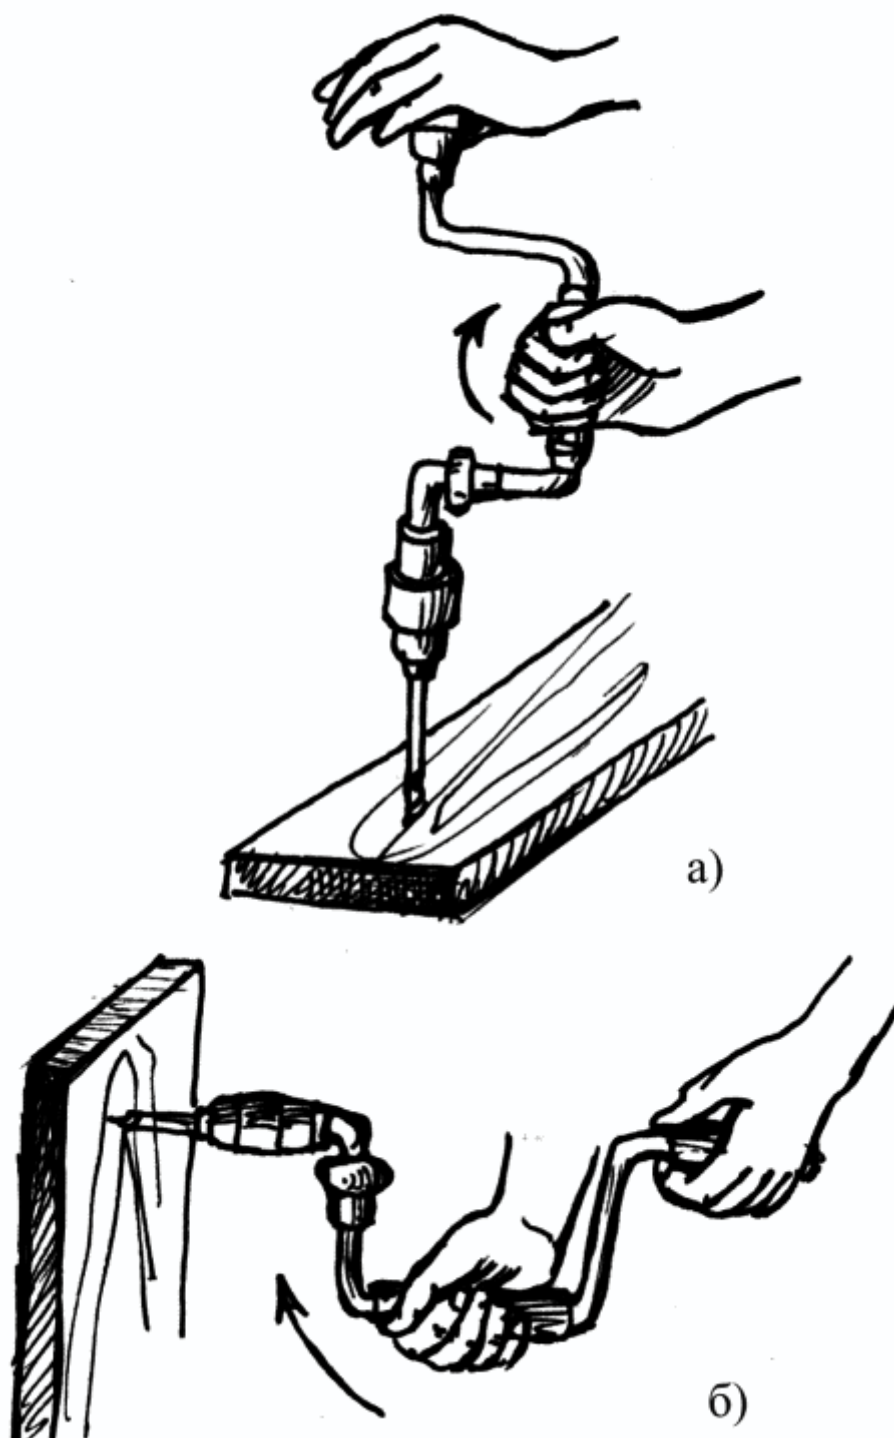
Приемы сверления древесины коловоротом: а – при горизонтальном положении детали; б – при вертикальном положении детали, зажатой струбциной
